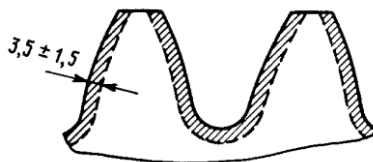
Профиль закаленного слоя зуба шестерни
